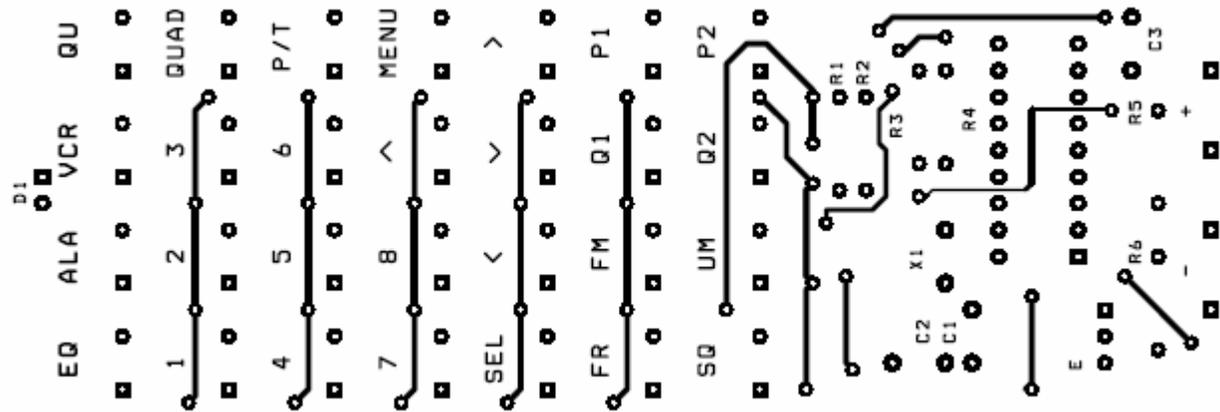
Circuito impreso del control remoto (lado de los componentes).
